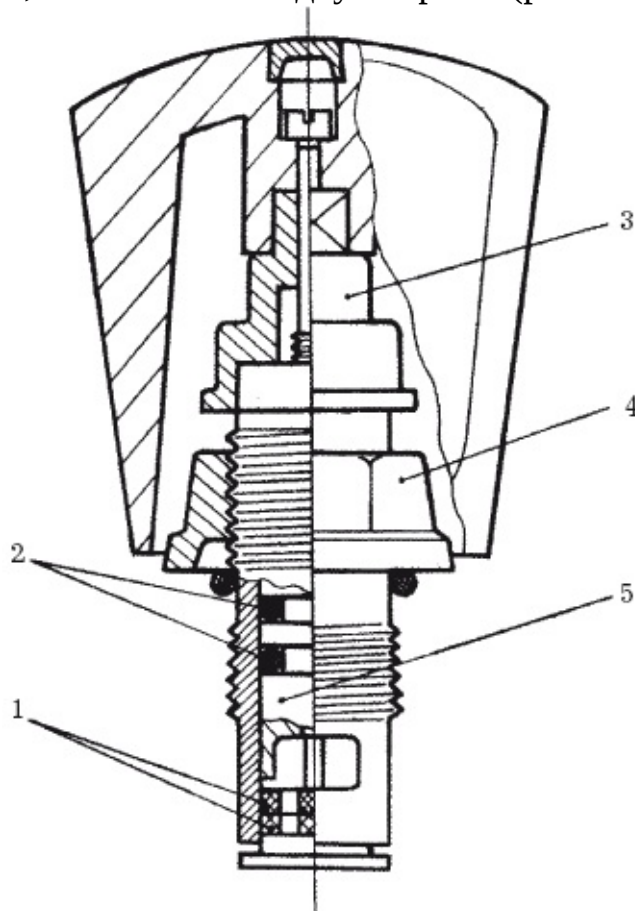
Головка крана с керамическими дисками: 1 – притертые керамические диски; 2 – уплотнительное кольцо; 3 – механизм поворота; 4 – регулирующая гайка; 5 – поворотный цилиндр из самосмазывающейся пластмассы
